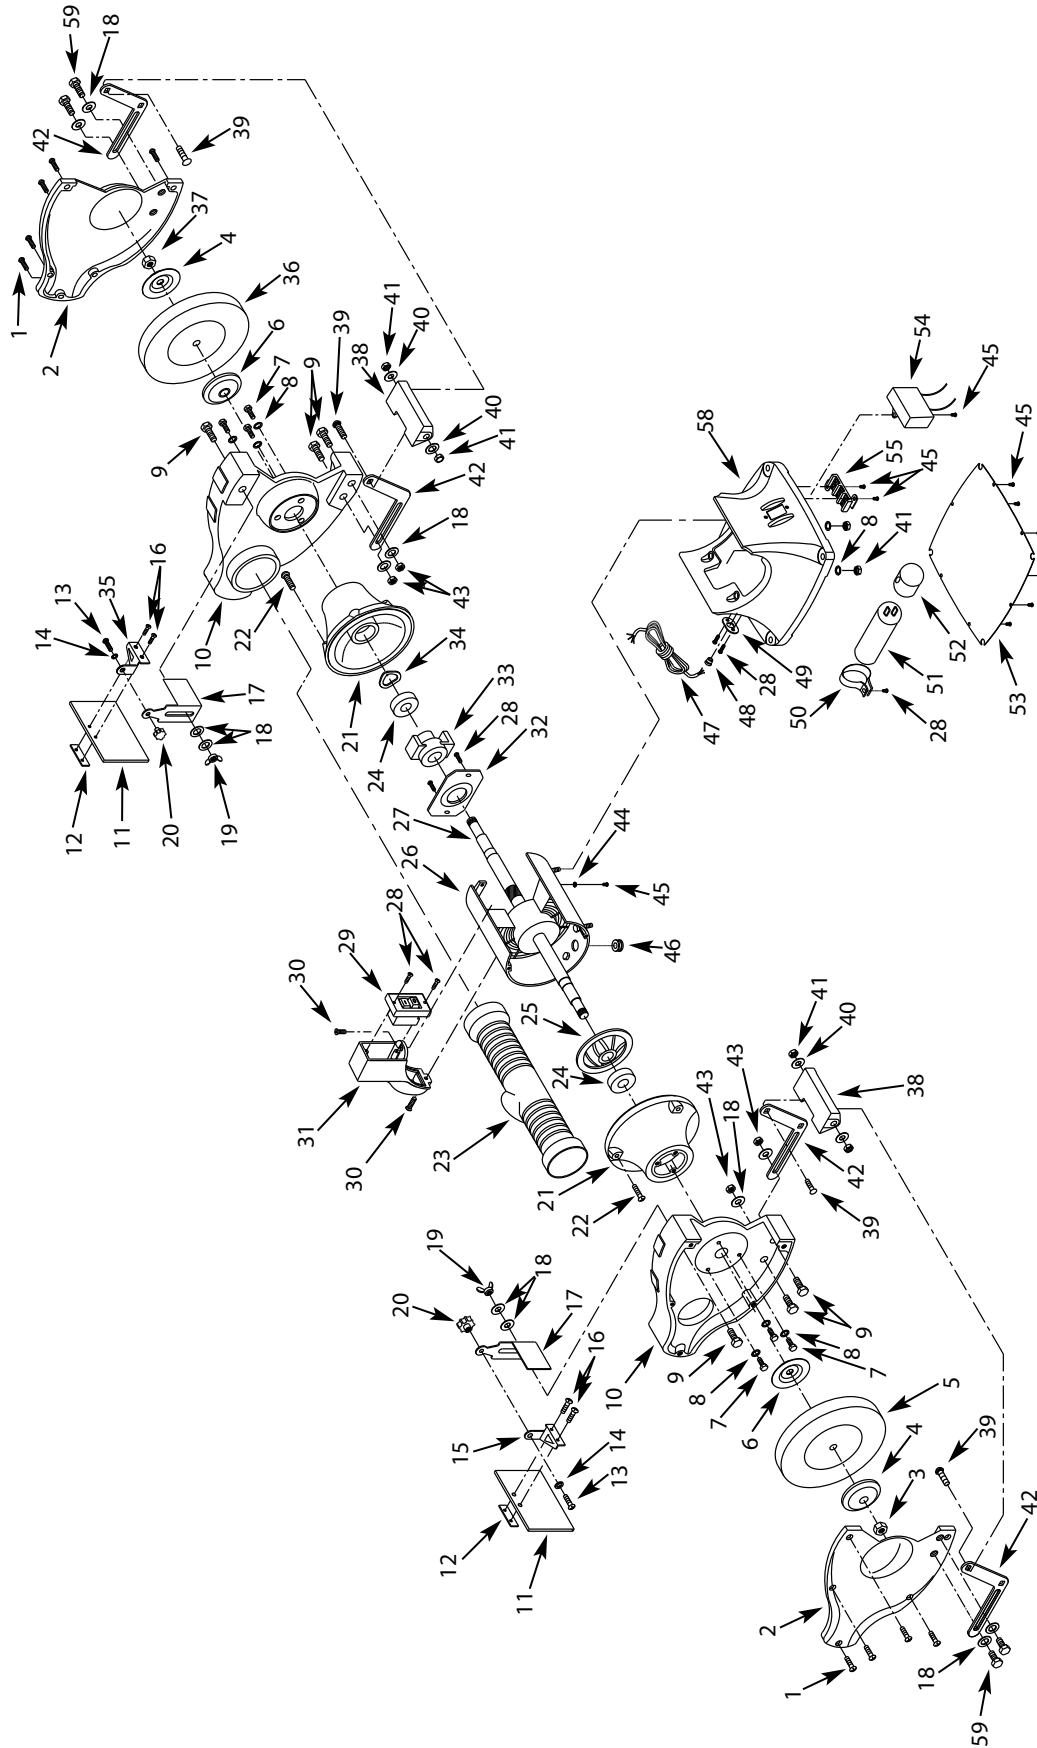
Illustration des pièces de rechange pour la meuleuse d'établi de 30,5 cm.
